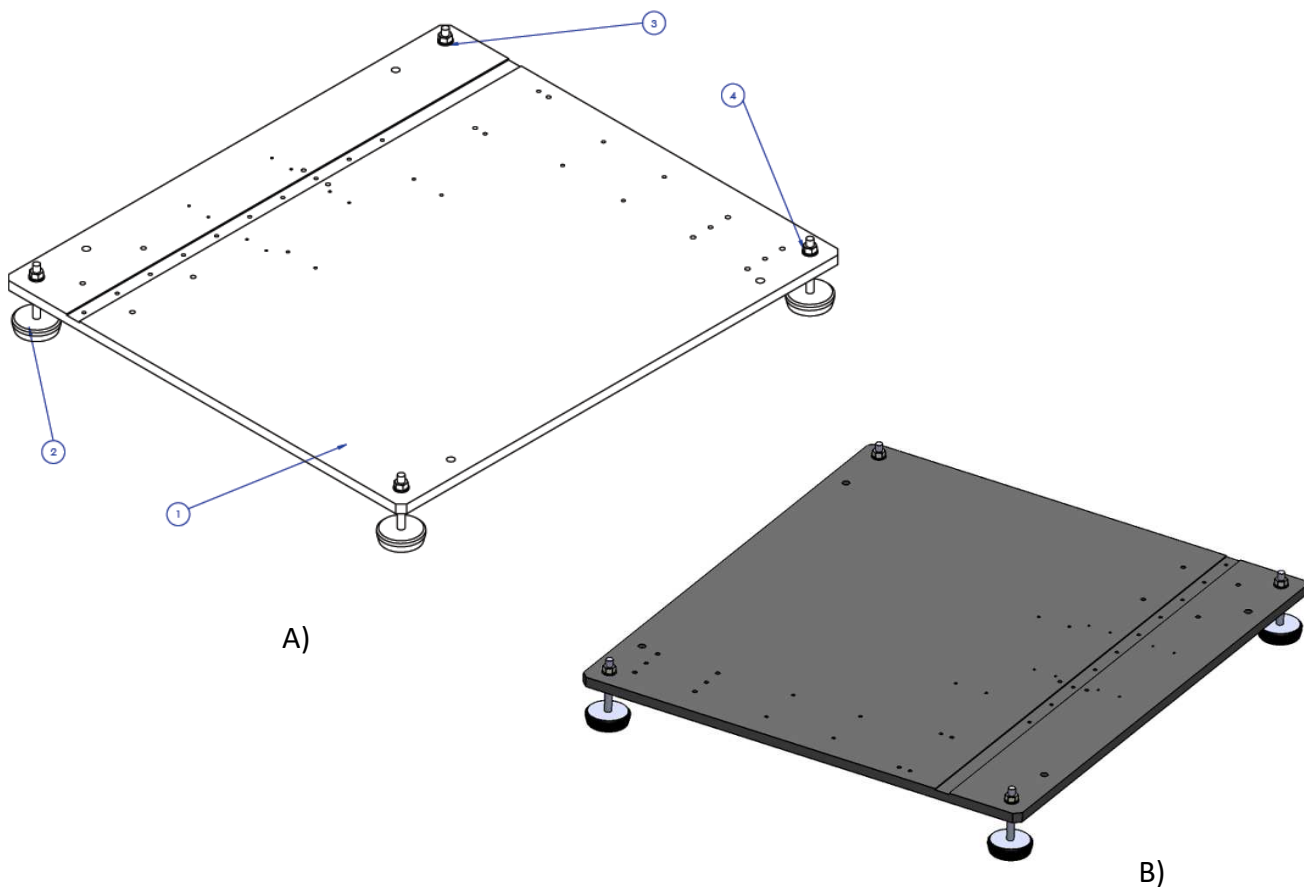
Bancada. A) Explosionado B) Conjunto bancada
